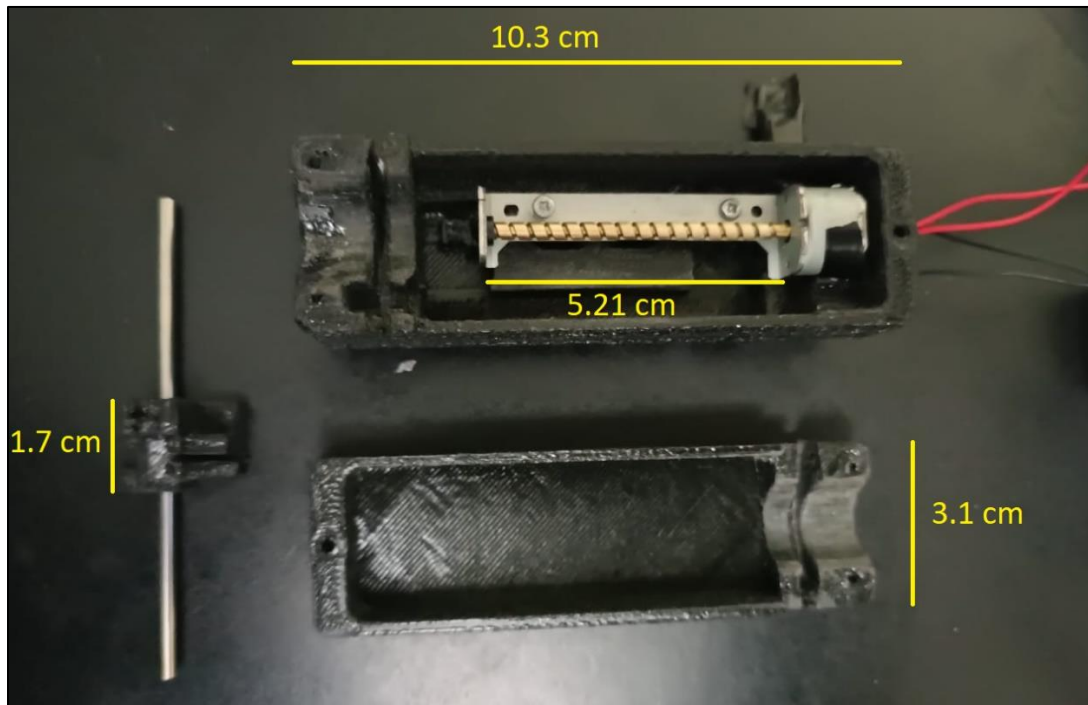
Dimensiones importantes de la estructura mecánica de soporte impresa en 3D con material PLA
